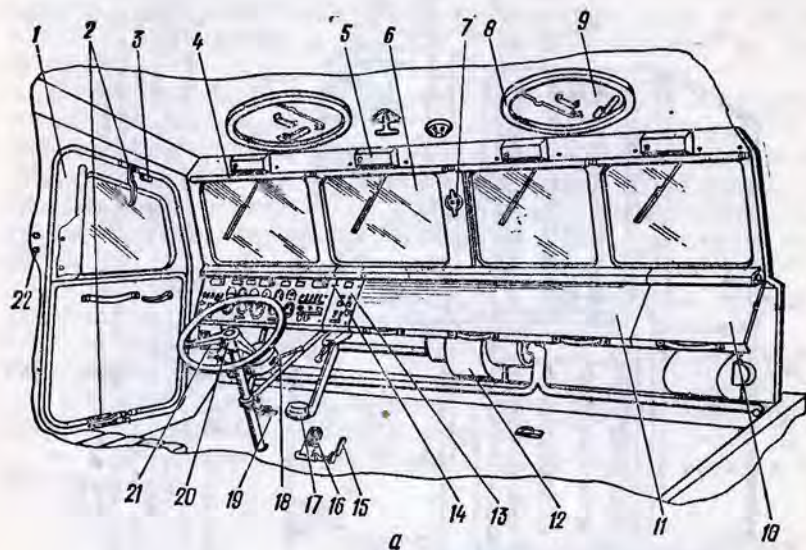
Корпус первого звена транспортера ДТ-10П:
